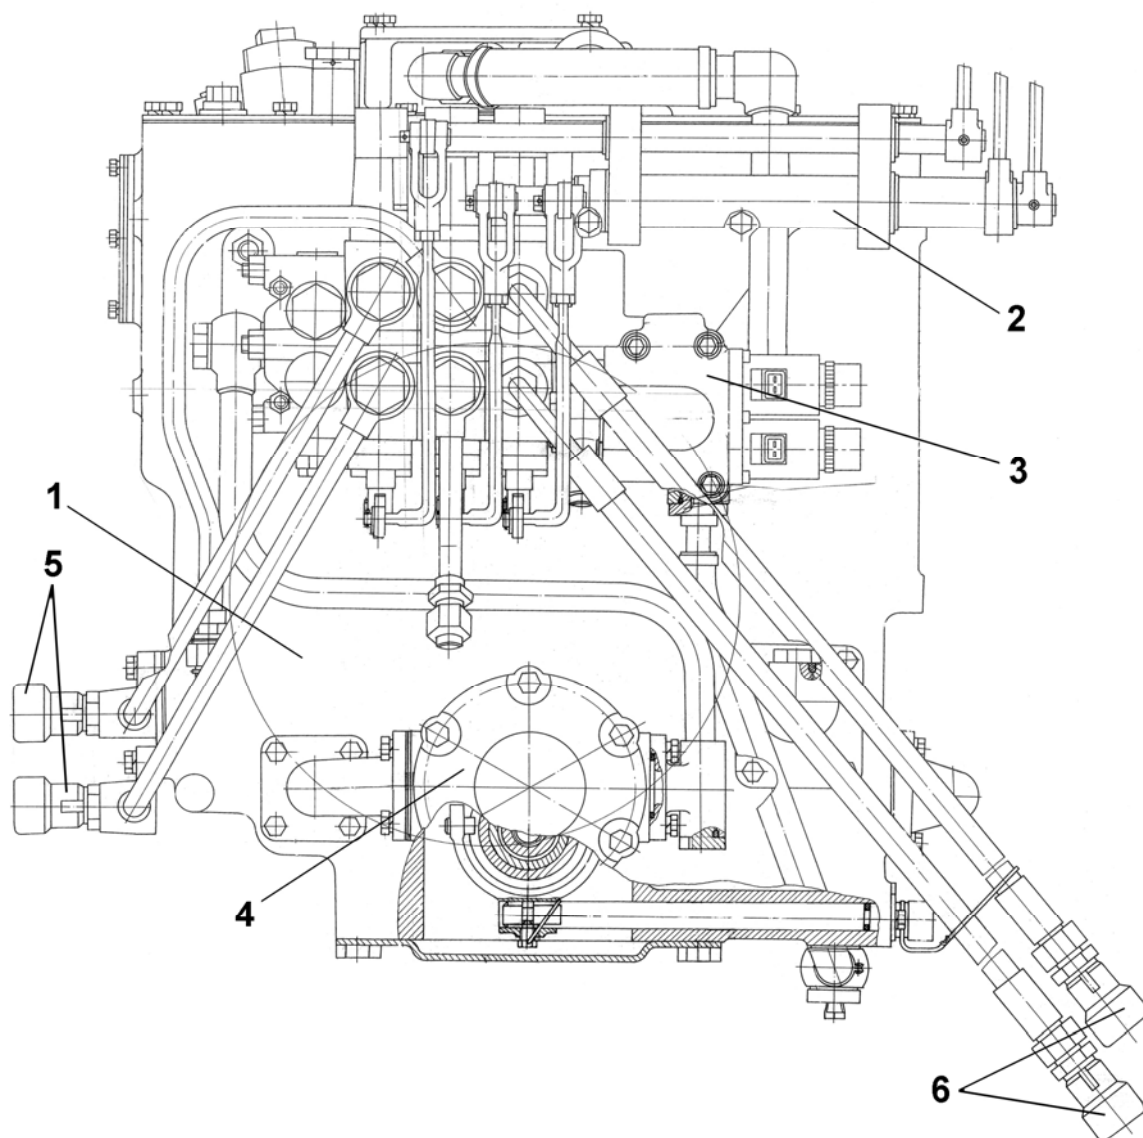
Корпус гидроагрегатов с агрегатами в сборе.
